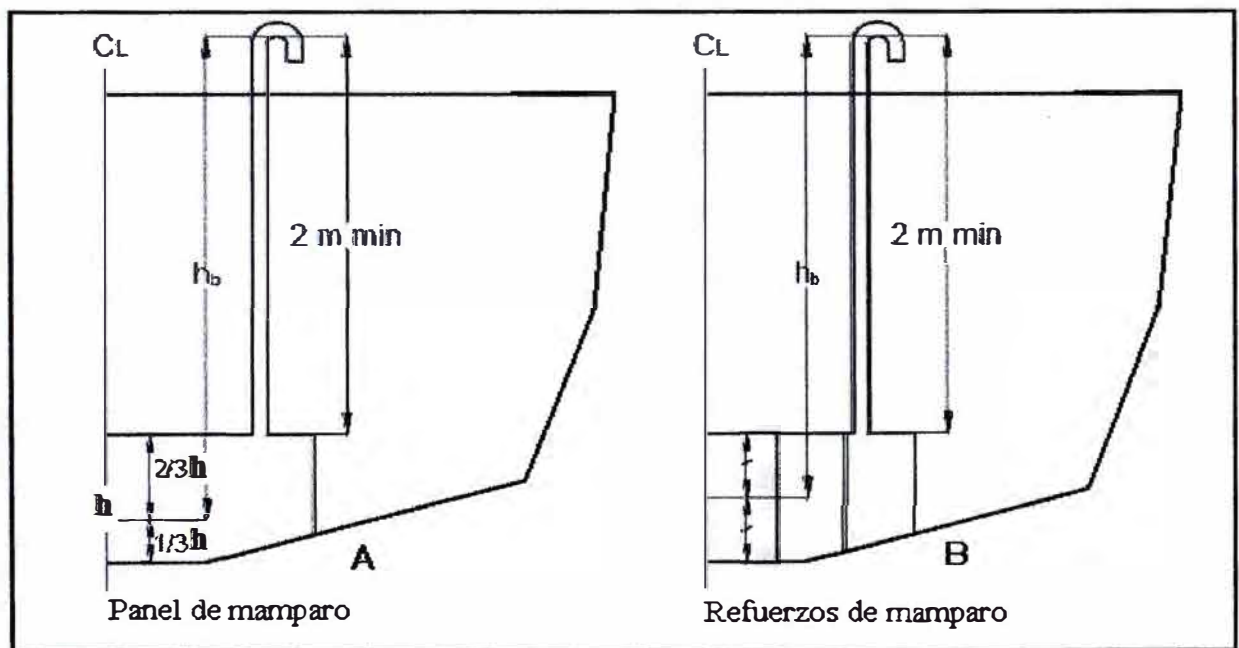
Medidas o dimensiones para el cálculo de la presión de diseño de mamparos de tanque [24].
